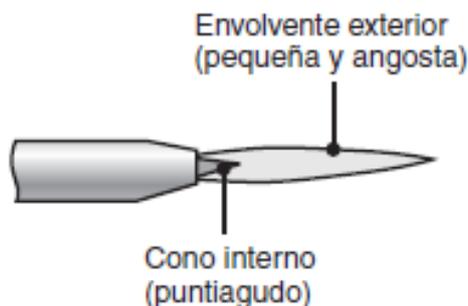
Llama oxidante (Fuente: *Manufactura, Ingeniería y Tecnología*)
